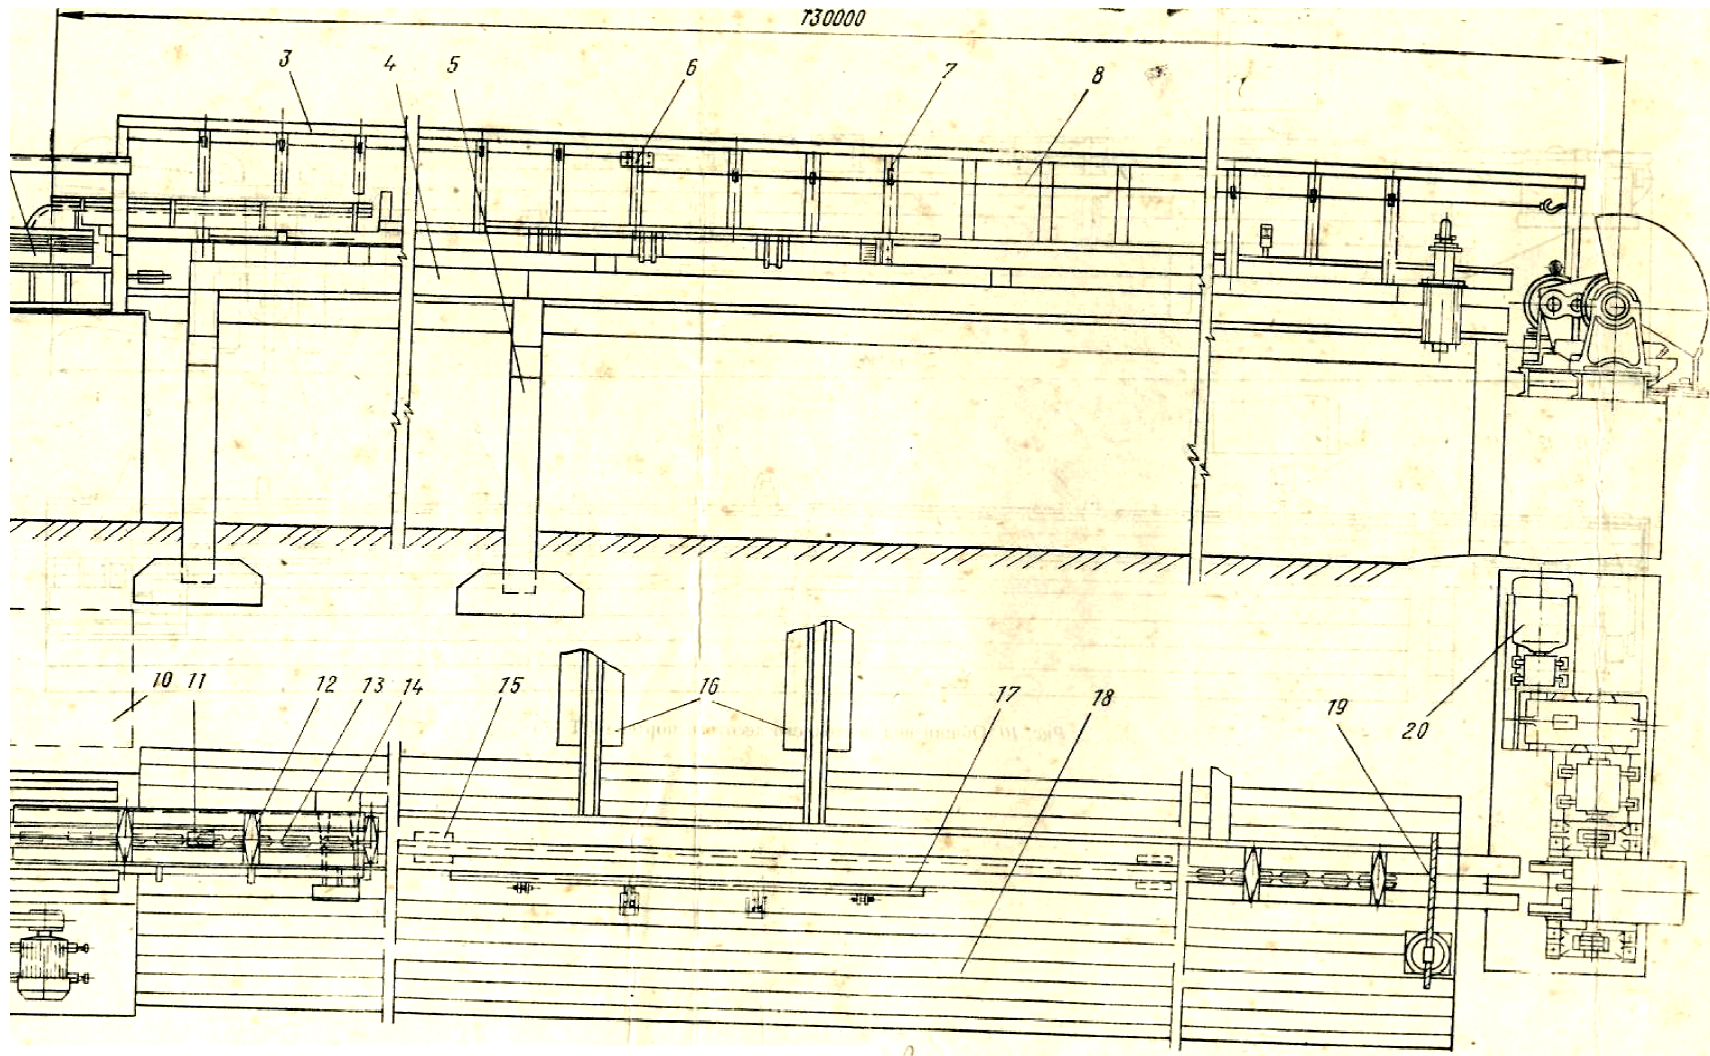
Общий вид лесотранспортера ЛТ-86А
